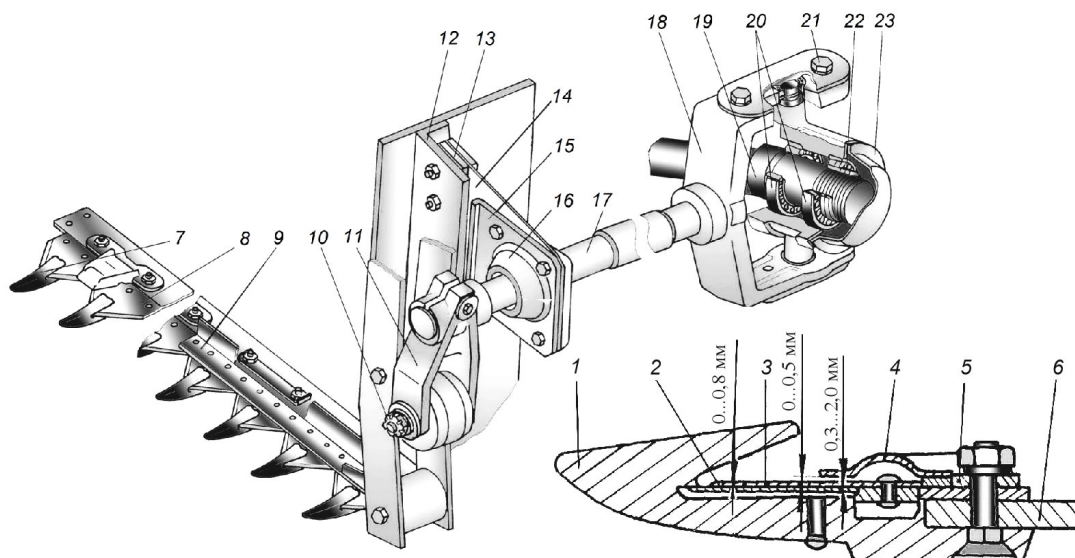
Механизм «качающейся шайбы»: 1 – палец; 2 – противорежущая пластина; 3 – сегмент; 4 – прижим; 5 – регулировочная прокладка; 6 – пластина трения; 7 – пальцевой брус; 8 – нож; 9 – головка ножа; 10 – ось; 11 – вилка; 12 – уголок; 13 – регулировочные прокладки; 14 – кронштейн; 15 – промежуточная опора; 16 – корпус; 17 – вал колебателя; 18 – вилка колебателя; 19 – кривошипный вал; 20 – роликовый конический подшипник; 21 – болт; 22 – корпус; 23 – крышка
